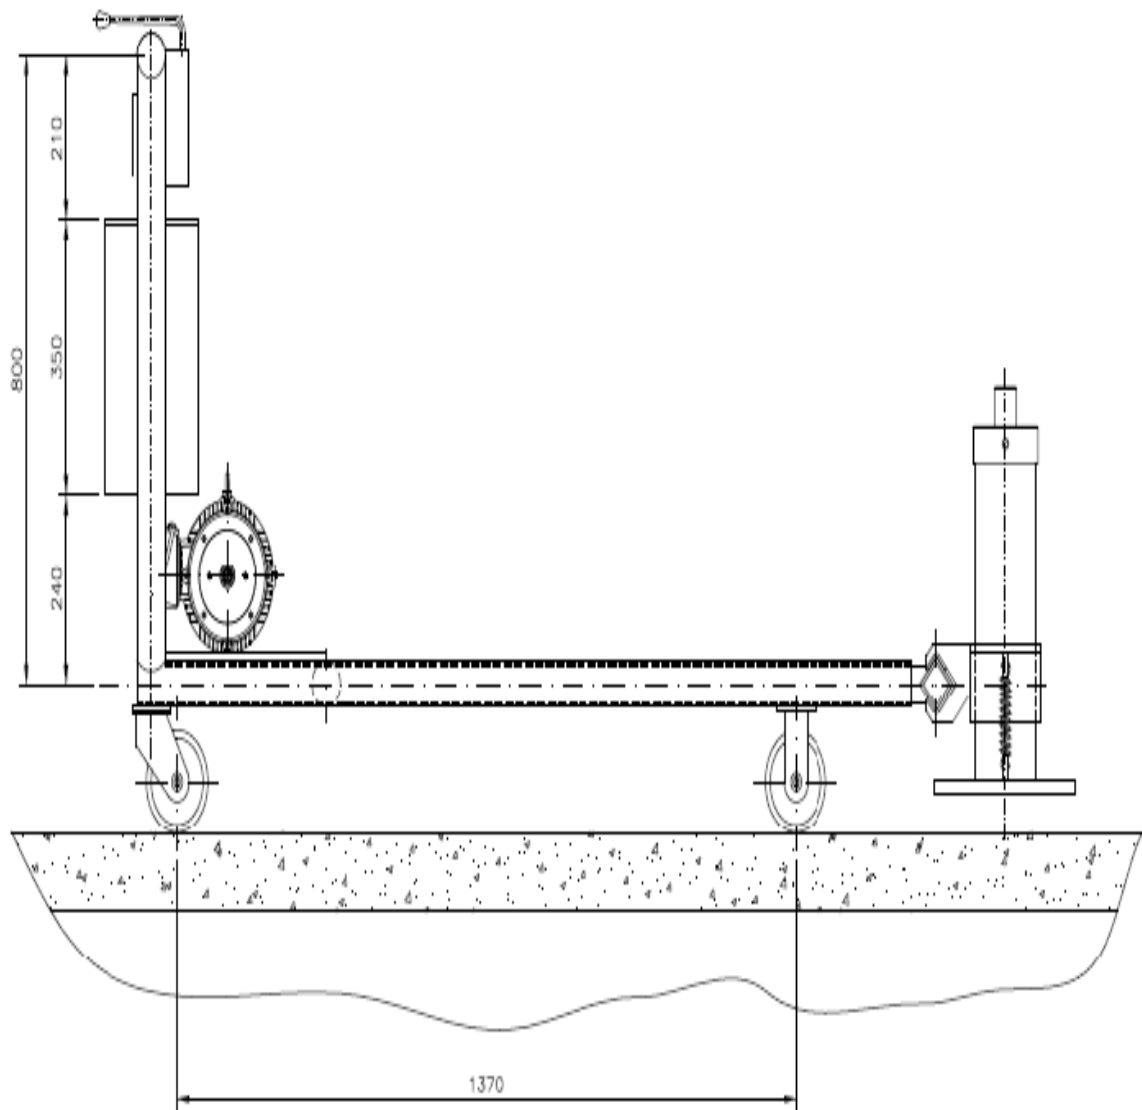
Dispositivo para Elevação, vista lateral. Escala 1:5, 2014.
